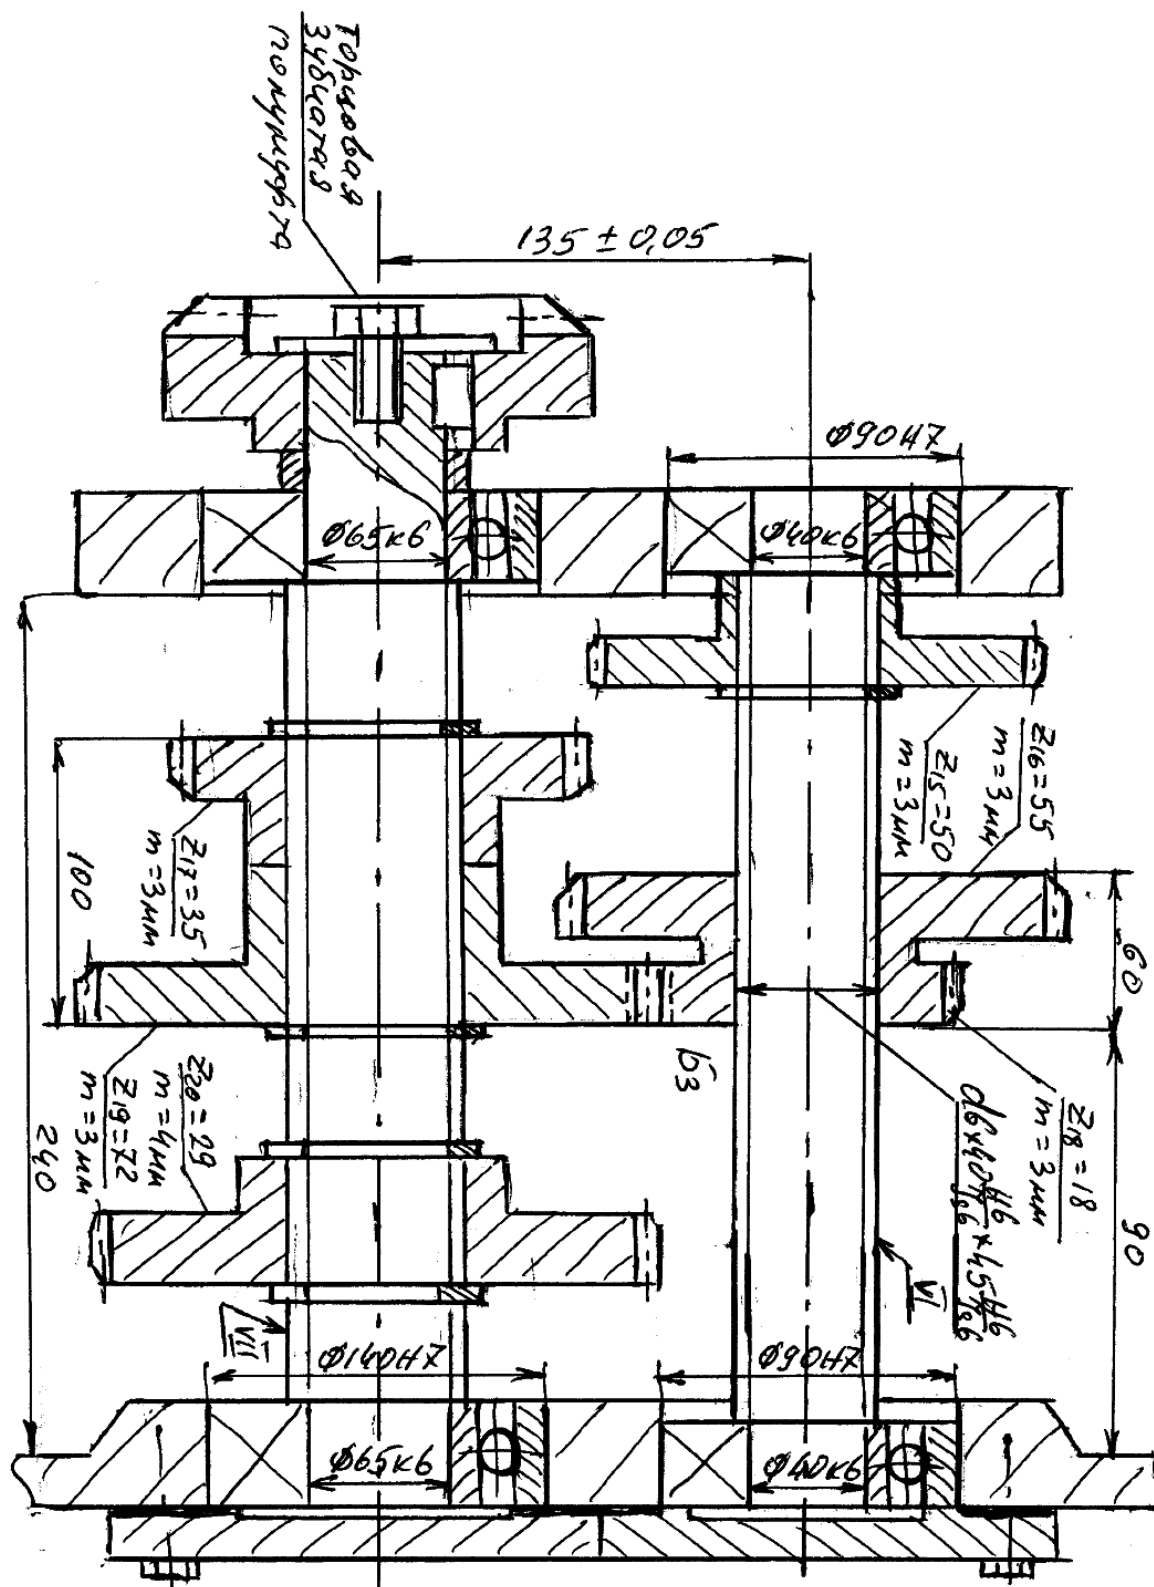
Сборочный чертеж наиболее нагруженной группы передач
